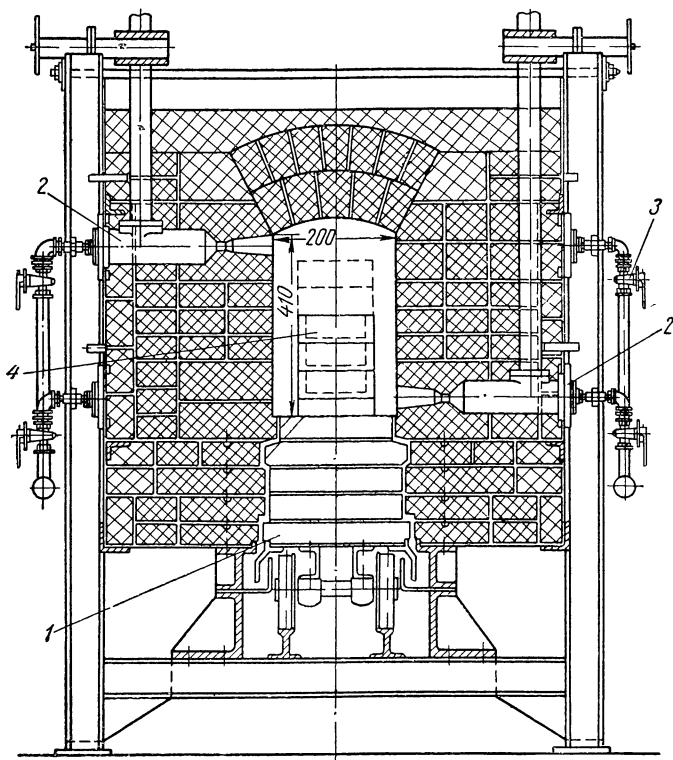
Поперечный разрез пламенной туннельной печи на газовом топливе.
